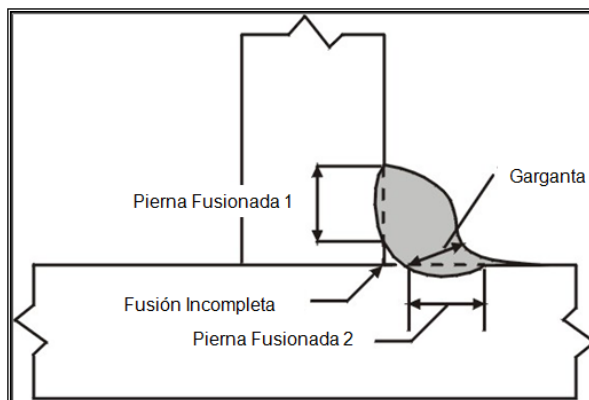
Unión en T con soldadura de filete con fusión incompleta^[1]
